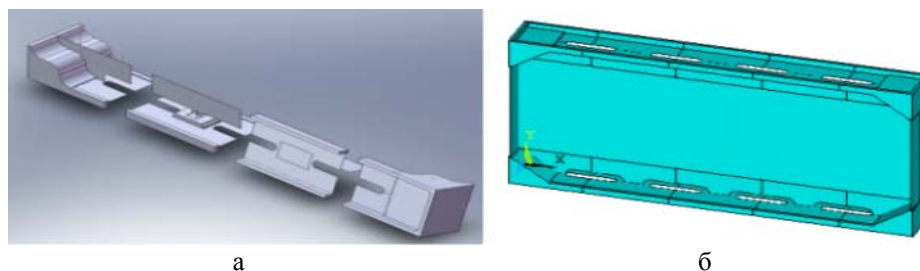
Конструктивные элементы корпуса рамки РЭА КА (а) и сборка корпуса рамки РЭА КА из конструктивных элементов (б)
